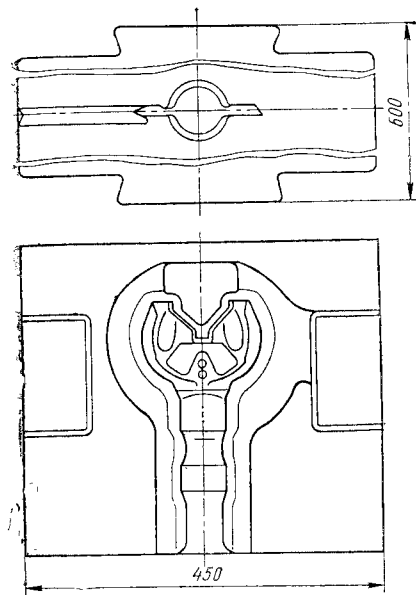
Ковочный штамп для штамповки полуоси переднего ведущего моста
